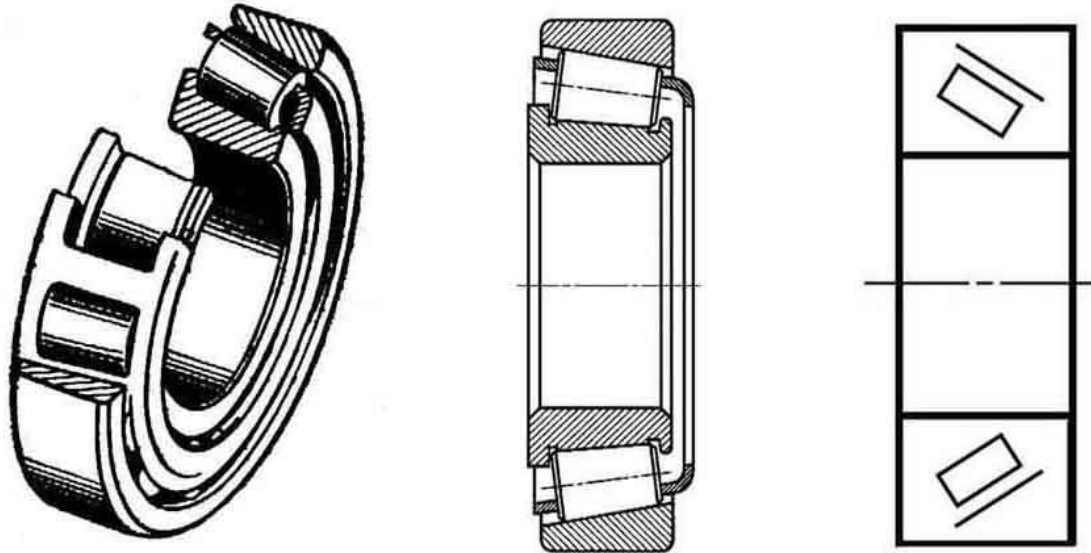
Підшипники конічні радіально-упорні типу 7000
